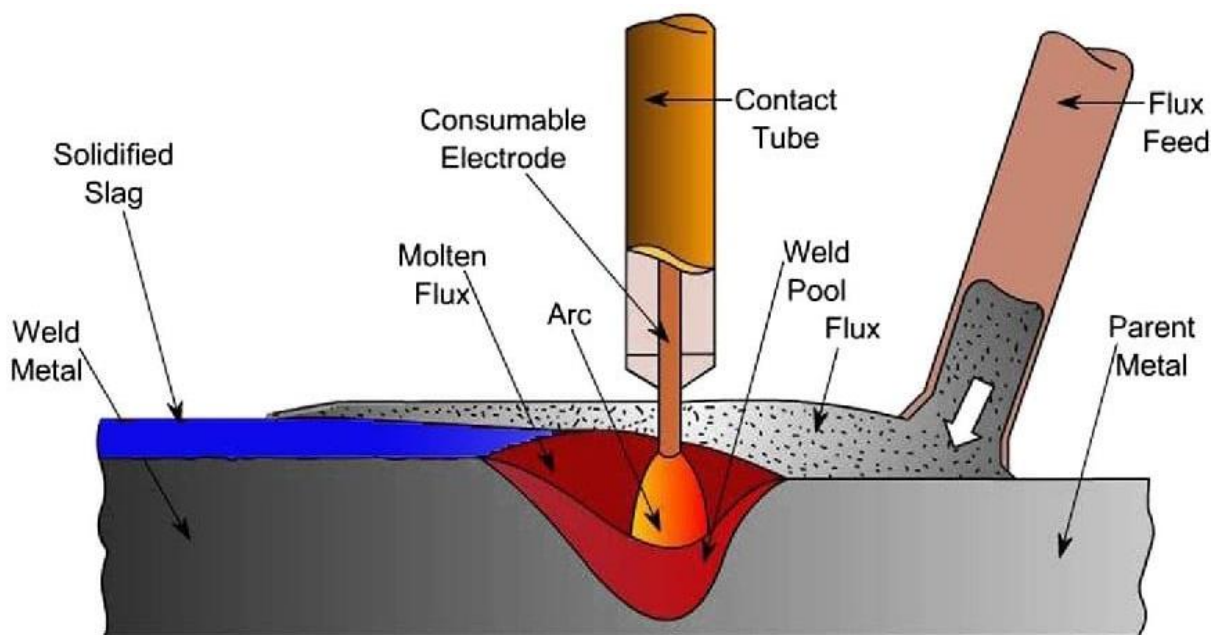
Схема выполнения автоматической сварки под флюсом
